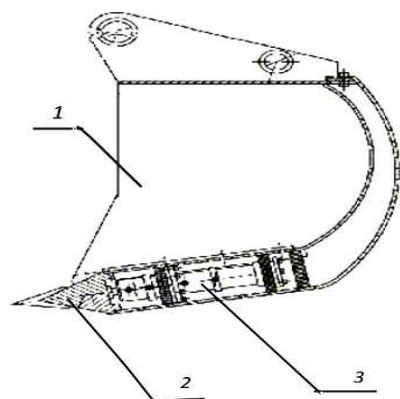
Конструкція ковша екскаватора з гідроударним пристроєм:
